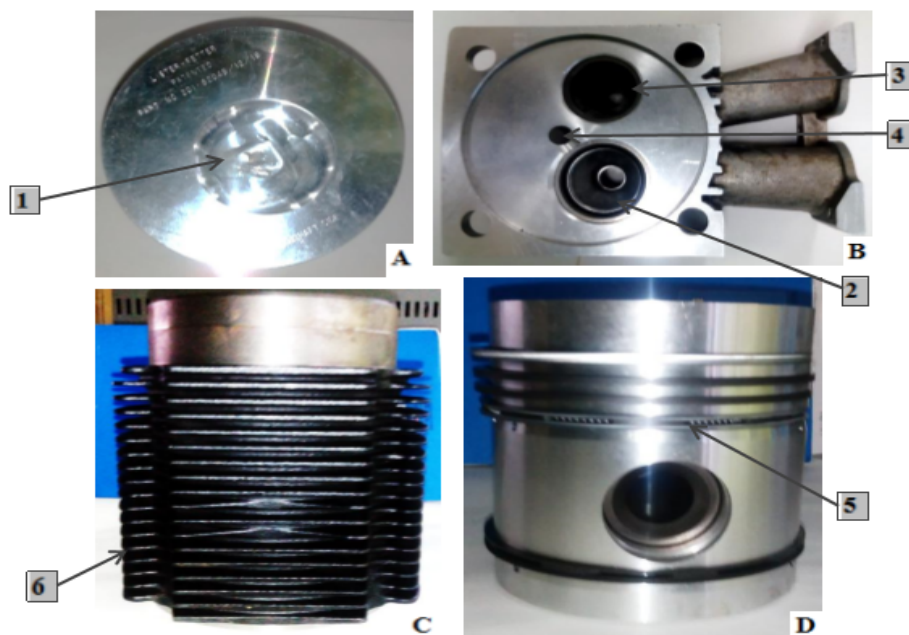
Composants de la chambre de combustion. A) Tête du piston ; B) Culasse ; C) Bloc moteur ; D) vue du piston.
